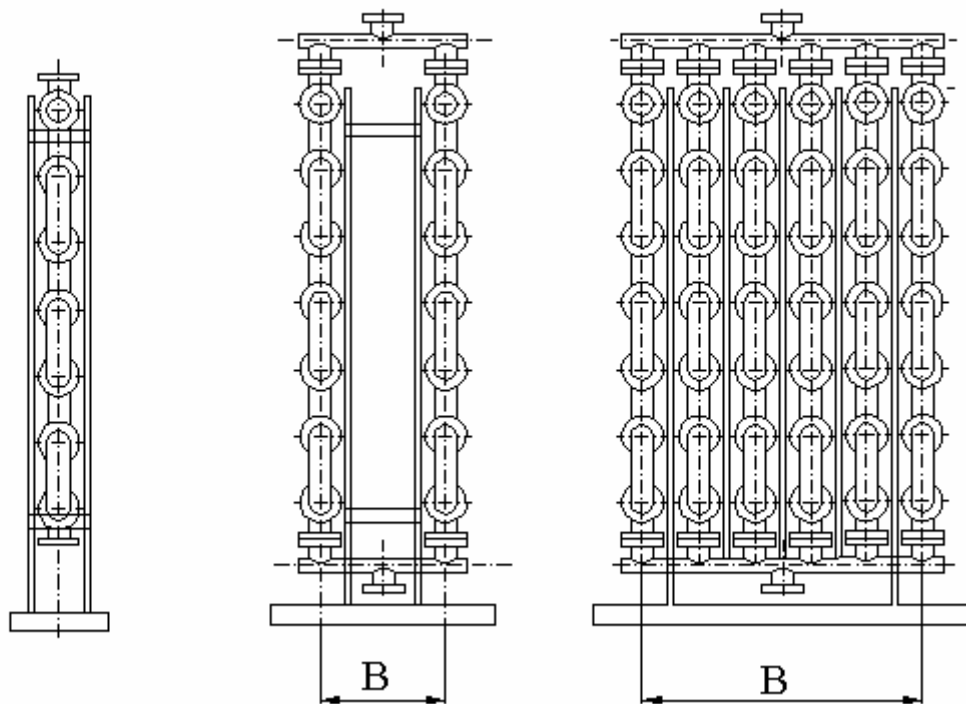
Сборочный чертеж теплообменника типа ТТ, вид сбоку
